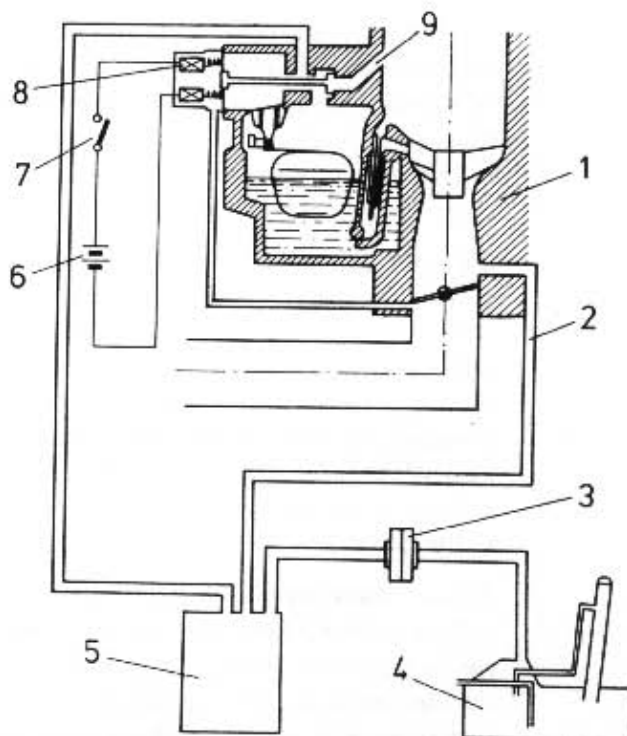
SPRAWDZANIE BIMETALOWEGO ZAWORU ODCINAJĄCEGO BVS
